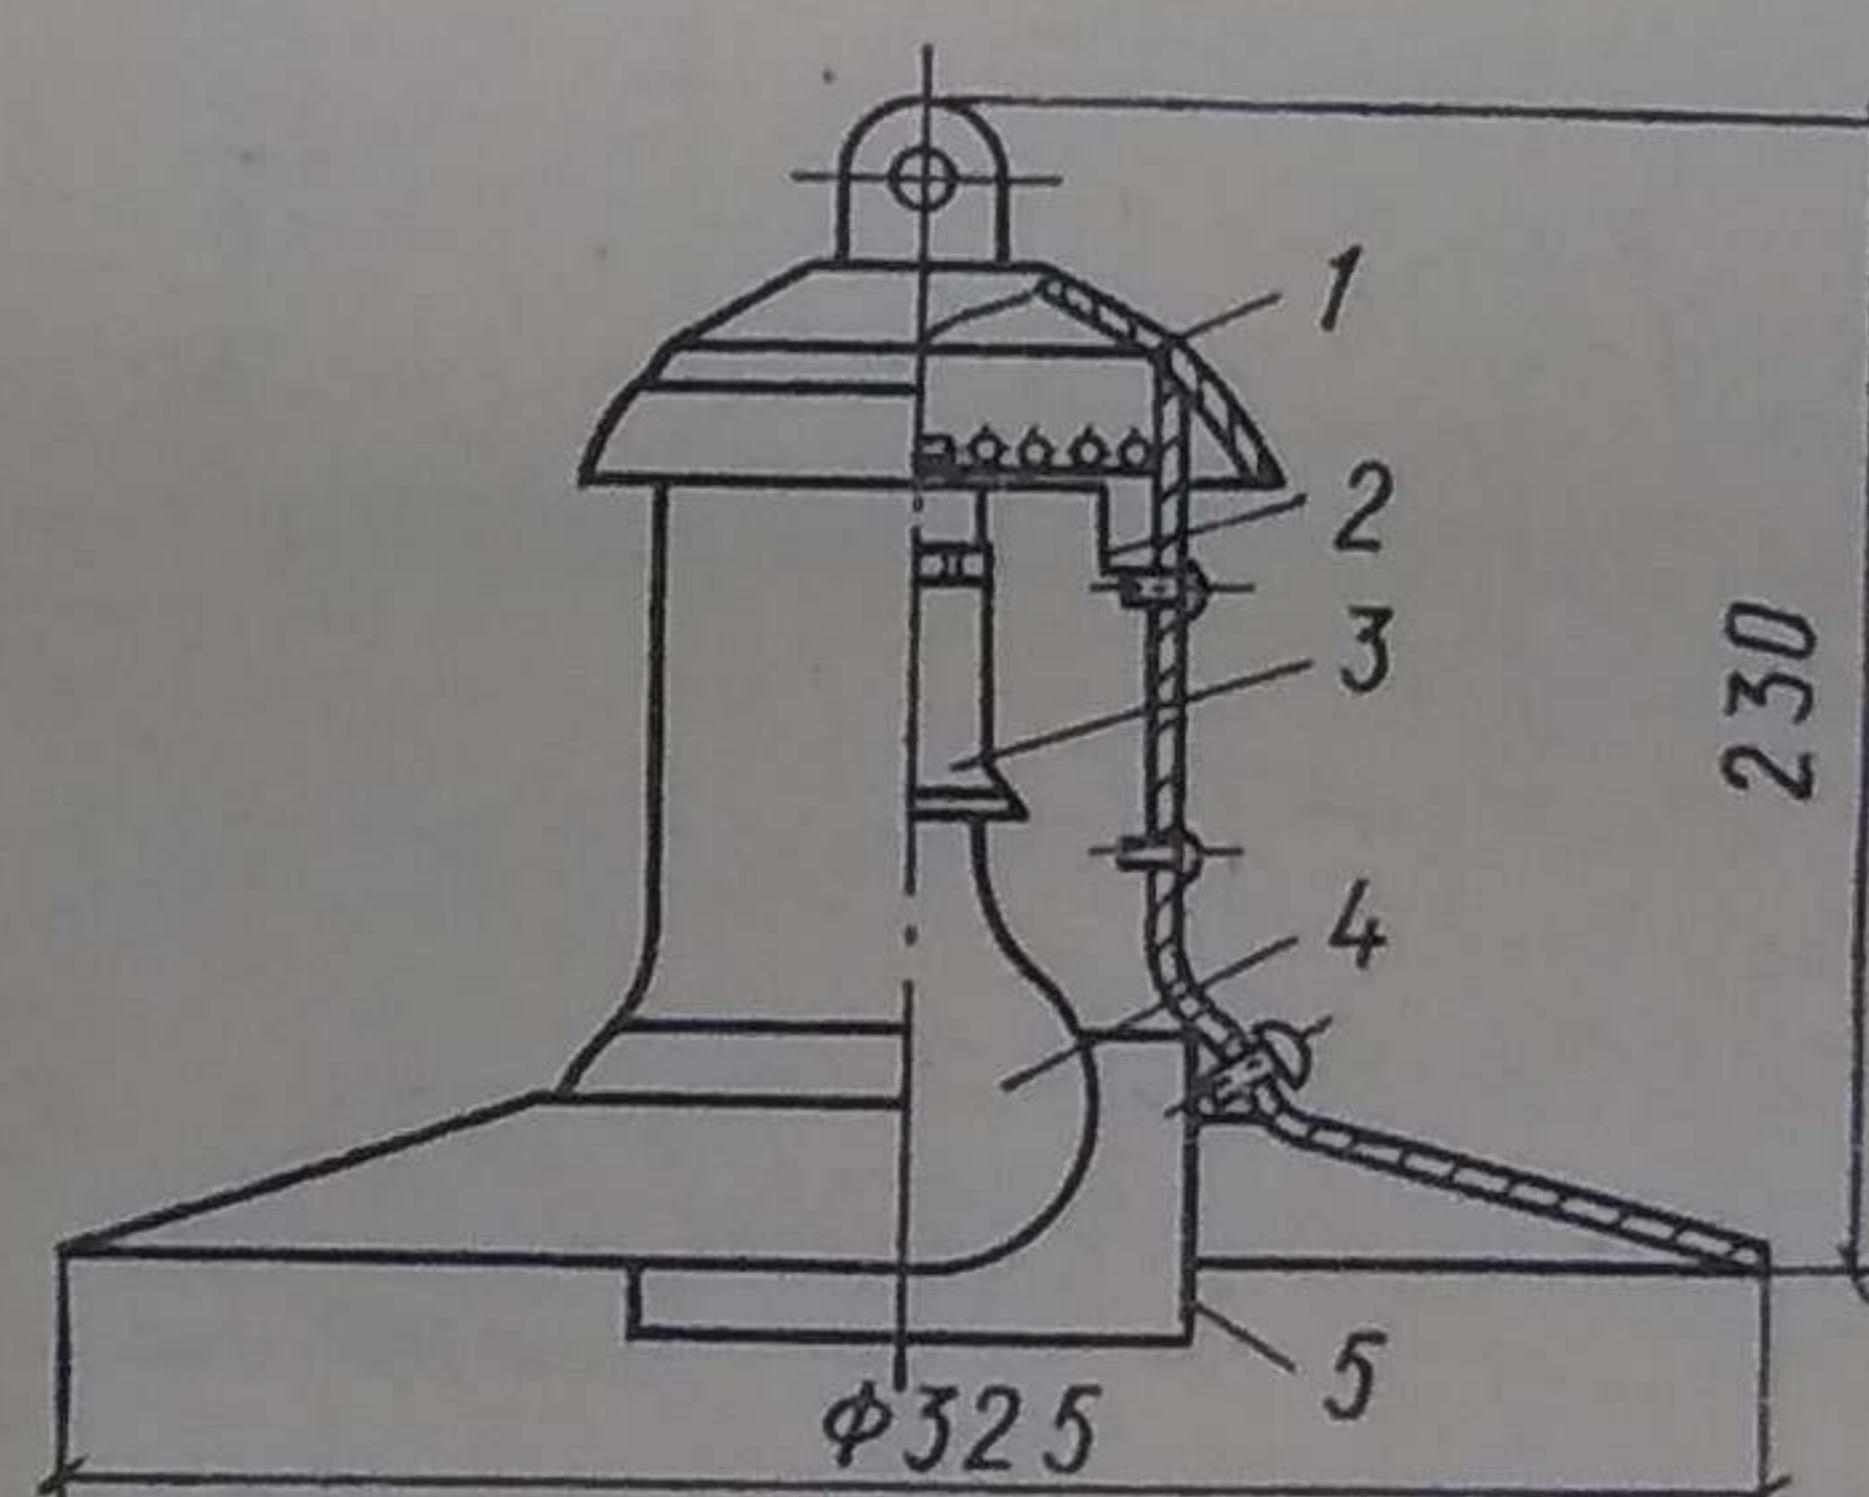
Светильник наружного освещения НО-300 с маскировочным приспособлением
